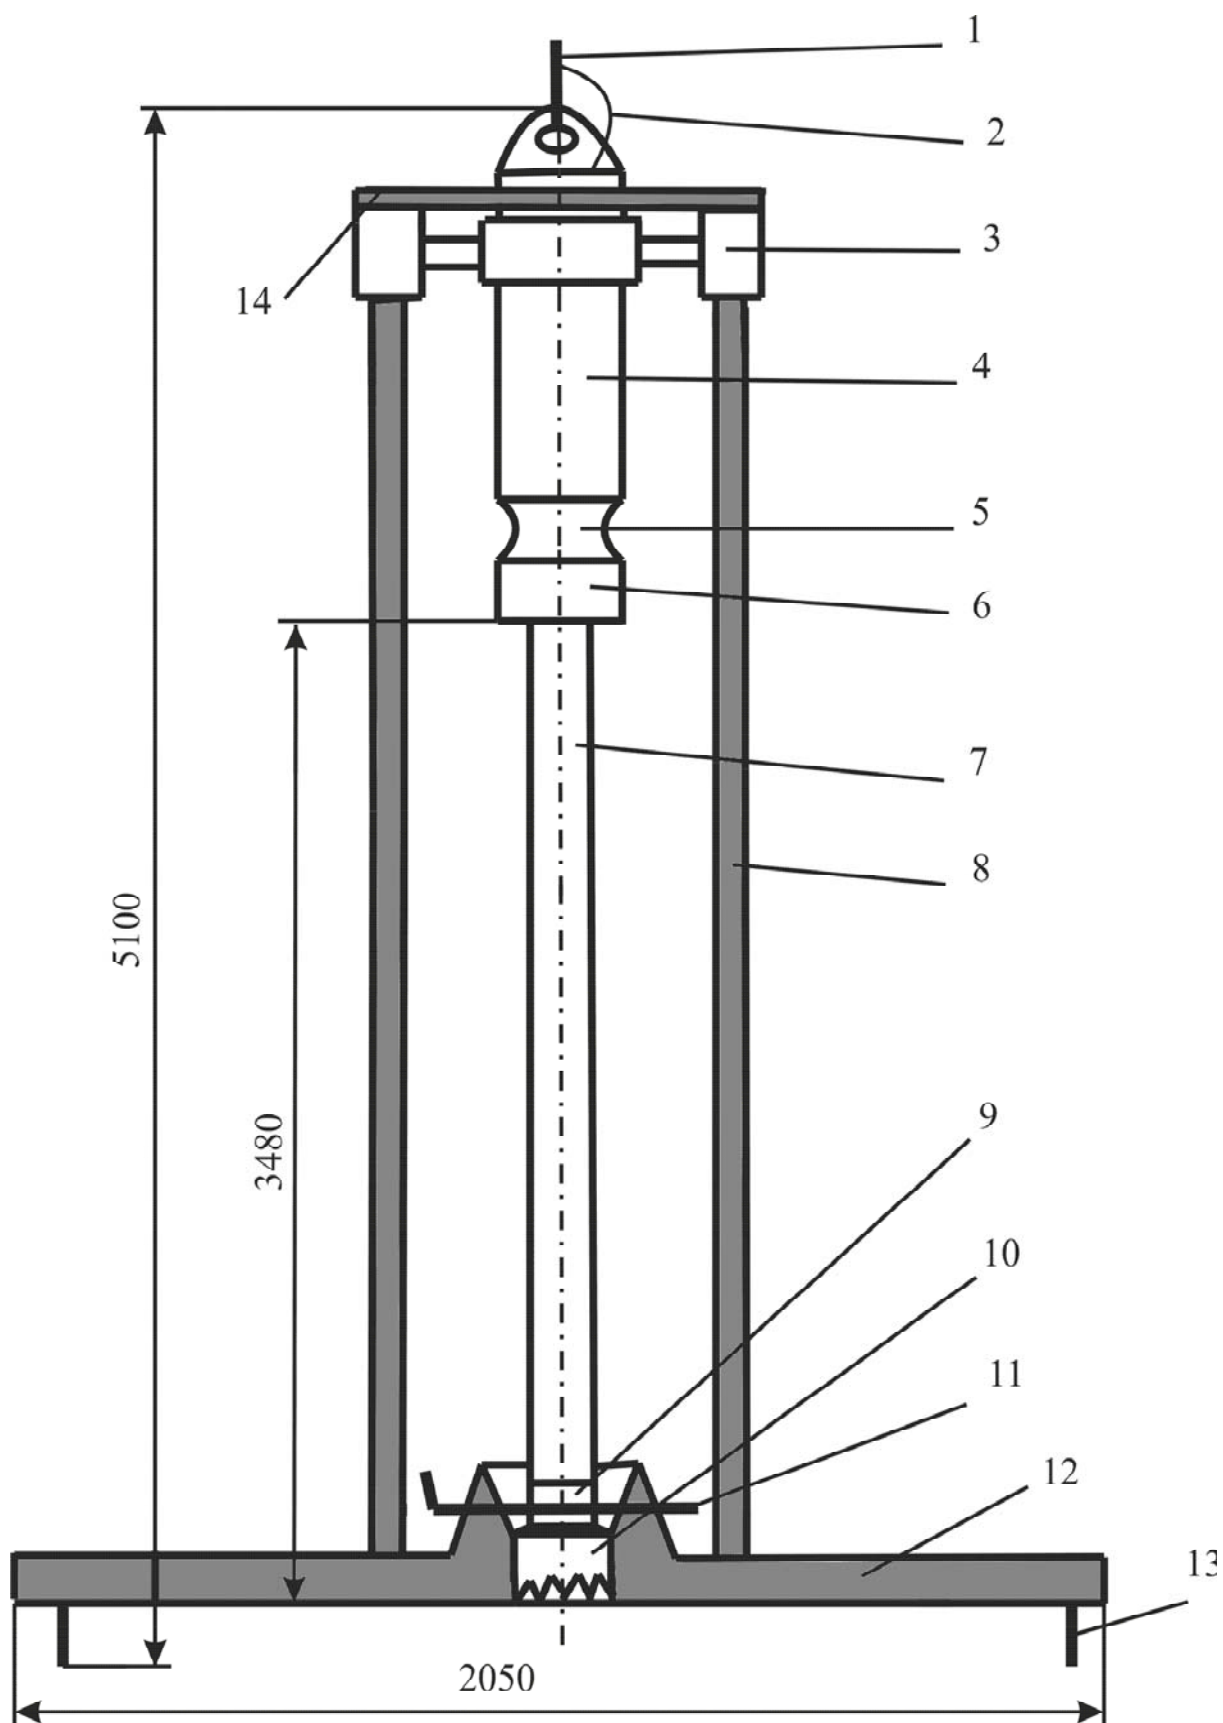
Схема установки для подводного бурения: 1-трос, 2-электрокабель, 3-штулка, 4-электродвигатель, 5-планетарный редуктор, 6-опорный узел, 7-колонковая труба, 8-направляющая труба, 9-затворное устройство, 10-коронка, 11-стопор, 12-опорная рама, 13-штырь, 14-траверса.
